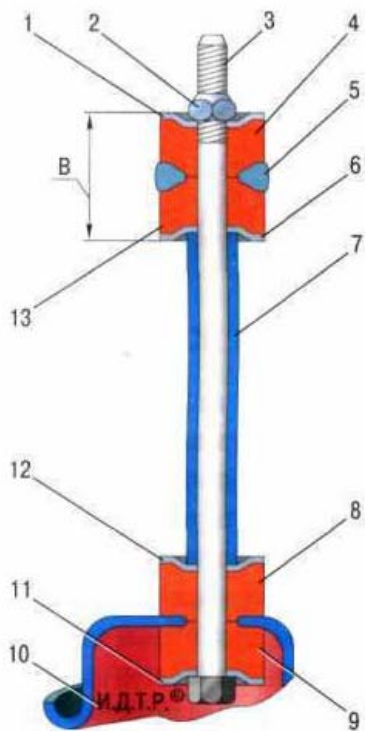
Стойка стабилизатора: 1, 6, 11,12 - шайбы; 2 - гайка; 3 - болт, 4, 8, 9, 13 - резиновый втулки; 5 - штанга стабилизатора; 7 - распорная втулка; 10 - нижний рычаг; В - монтажный размер
